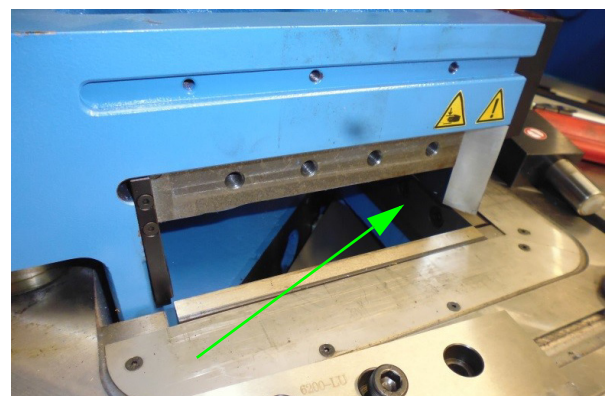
Zugang zu den Befestigungsschrauben des Untermessers
